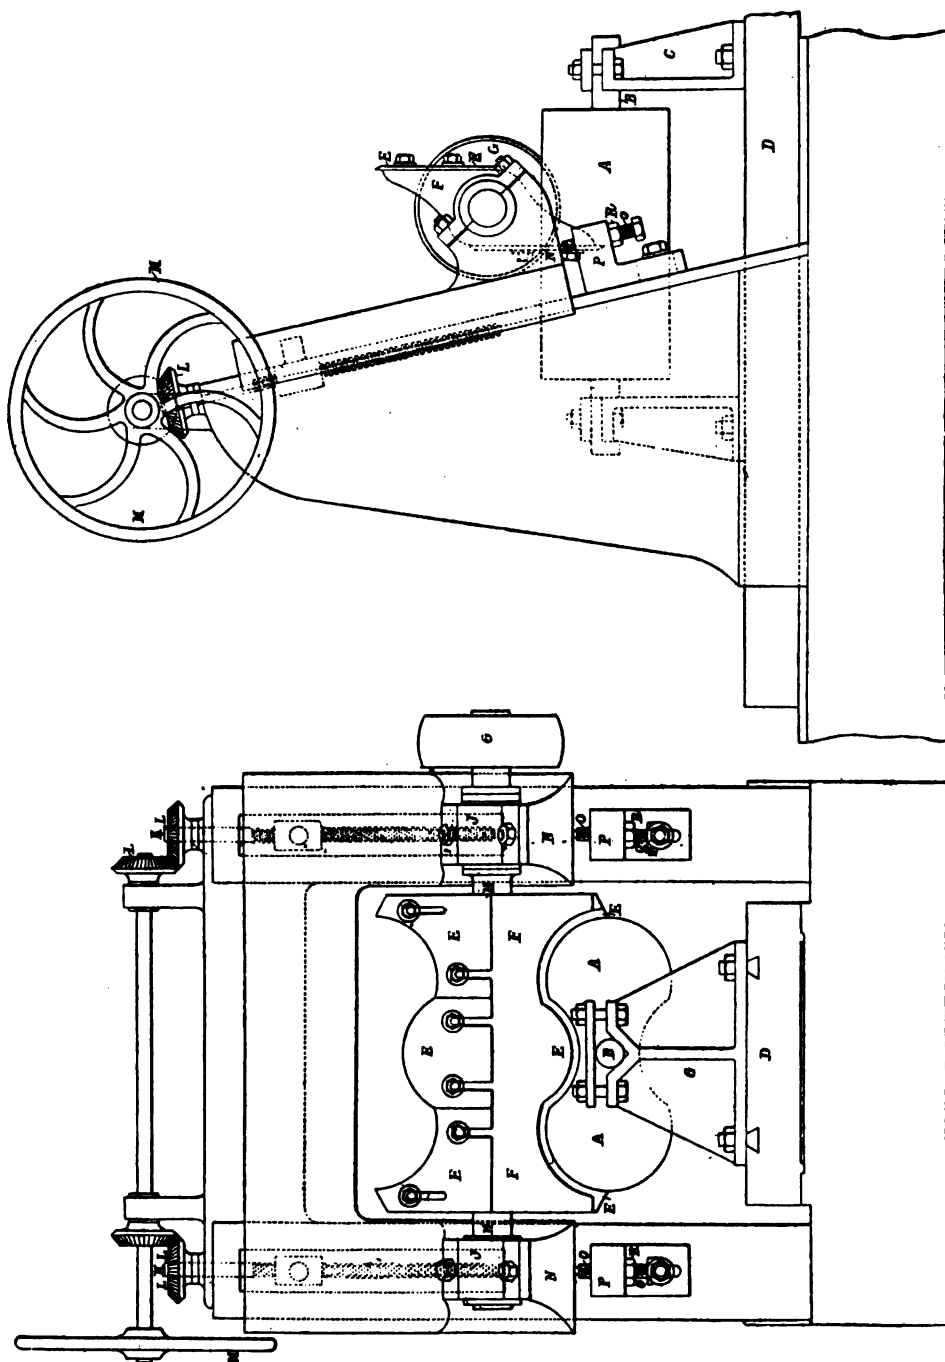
et 473. — Machine *Thwaites* pour la fabrication des pistons à surface en bois.
